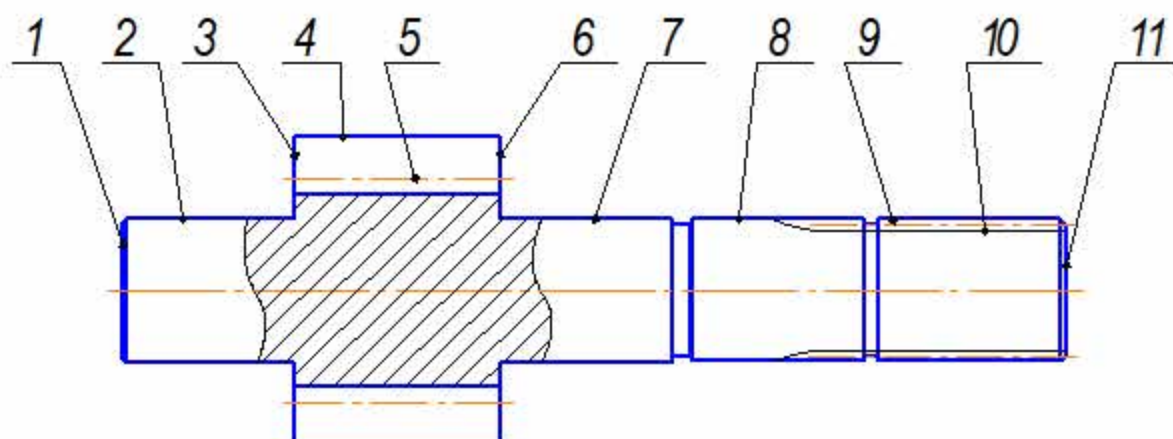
Ескіз деталі шестерня ведуча НШ32А-3-04
